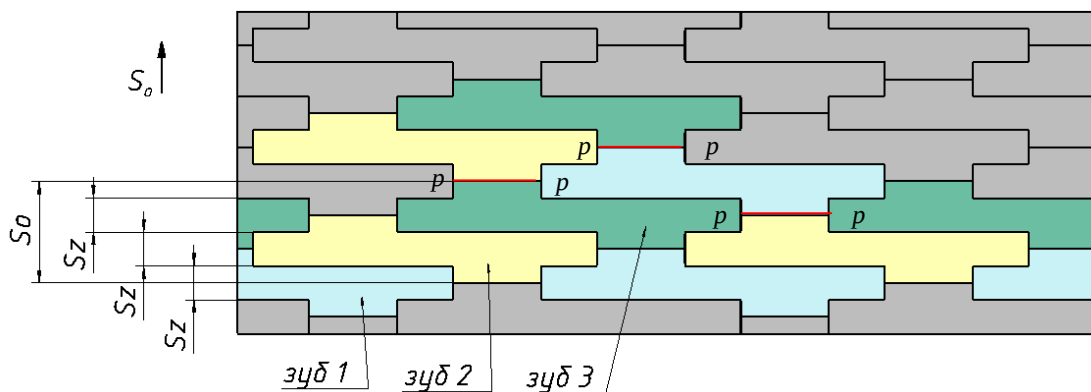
Вид поверхности, образованной фрезой с геометрией типа «Стружколом»
